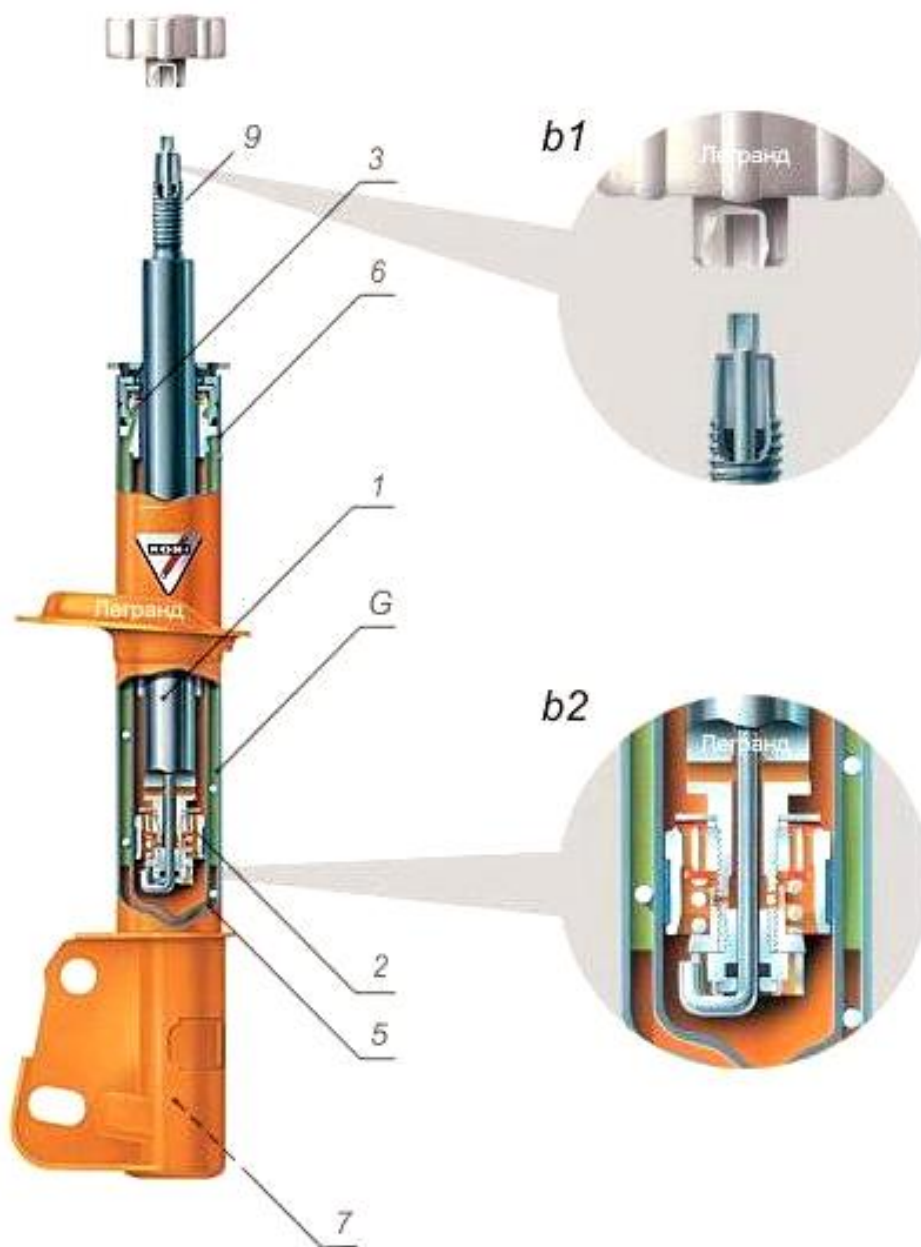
Двотрубний гідравлічний амортизатор
